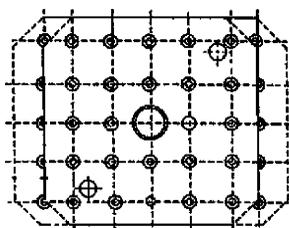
Станочная палета с резьбовыми отверстиями
